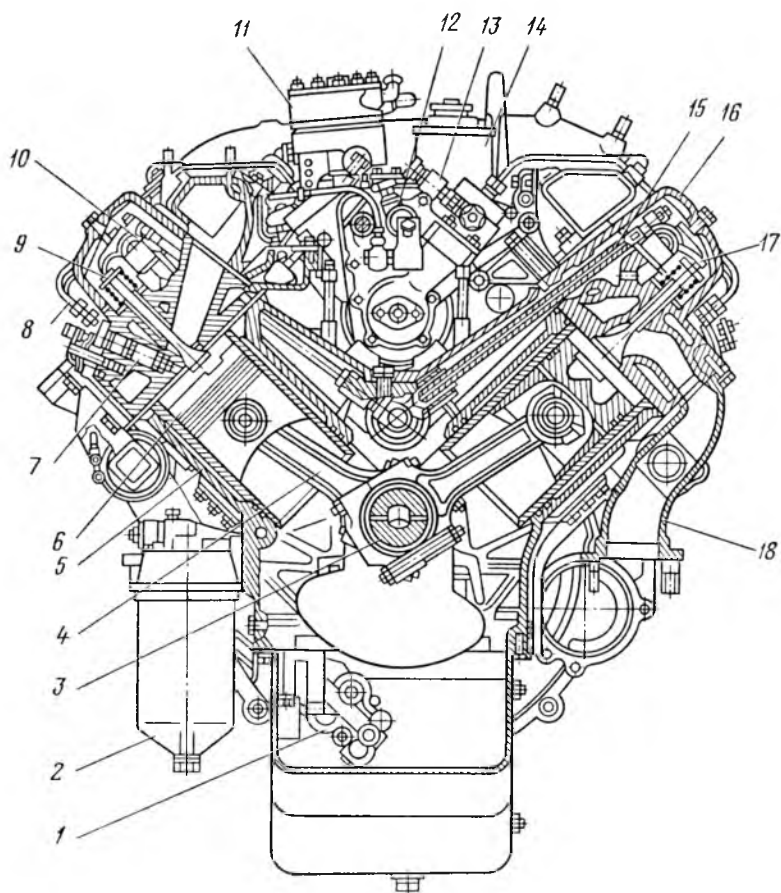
Поперечный разрез двигателя КамАЗ-7401:
